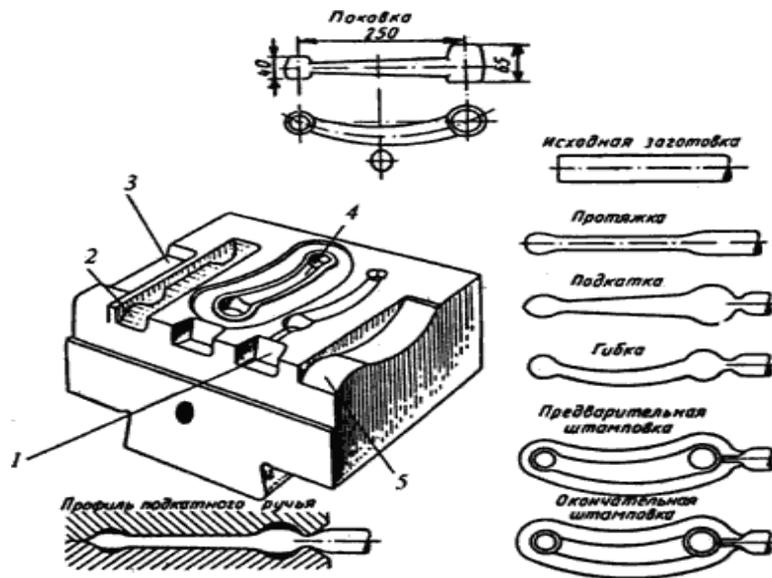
Стадии получения сложной поковки в нескольких ручьях
